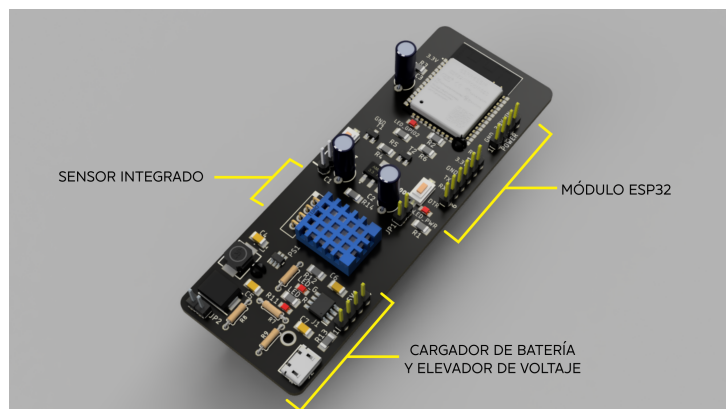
Montaje y distribución frontal del Módulo Wi-Fi con sensor integrado DHT11 v1.0.
